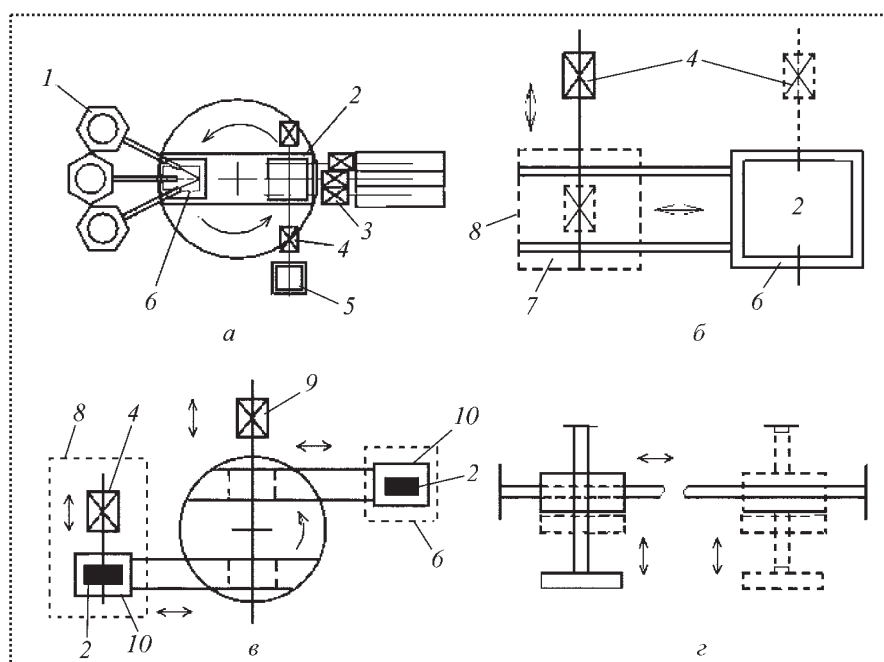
Схемы типовых унифицированных узлов линии сборки-сварки кузовов:
